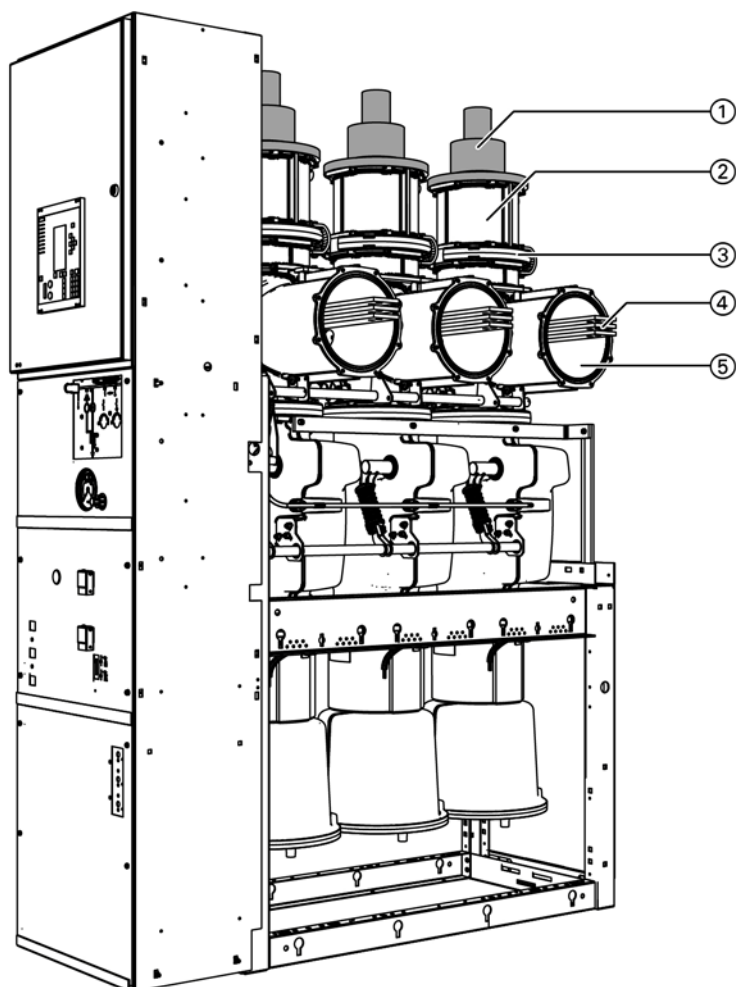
Обзор компоновки сборных шин: шина с элегазовой изоляцией без трехпозиционного разъединителя
